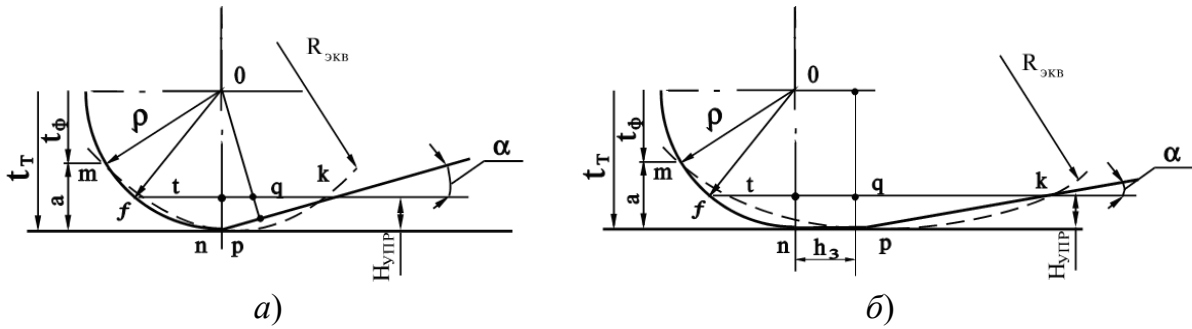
Схема контакта заточенного (а) и изношенного (б) резца с обрабатываемым изделием
